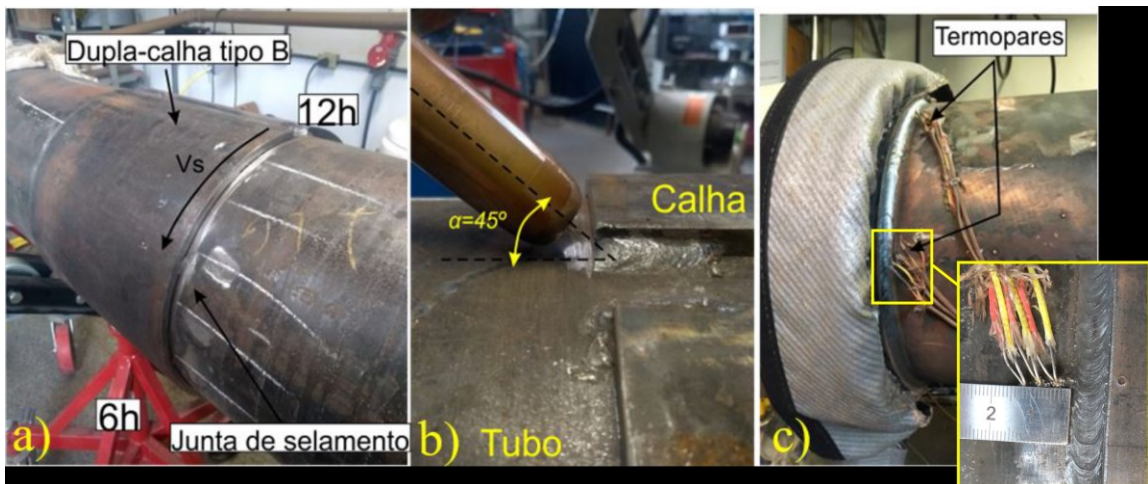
Soldagem de dupla-calha em ambiente de laboratório. Em a) Dupla-calha tipo B montada em circuito com água; b) Detalhe do posicionamento da tocha para soldagem; c) Posicionamento de termopares e medição com escala graduada após a soldagem.
